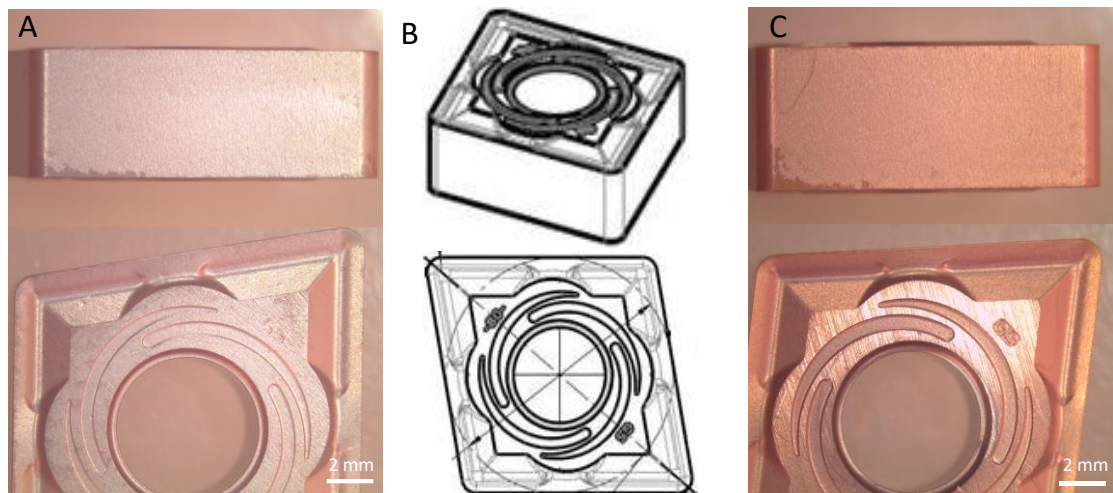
A) Pastilha de corte de WC-Co; B) Desenho técnico das pastilhas; C) Pastilha de corte de WC-Co revestida com TiAlSiN.
